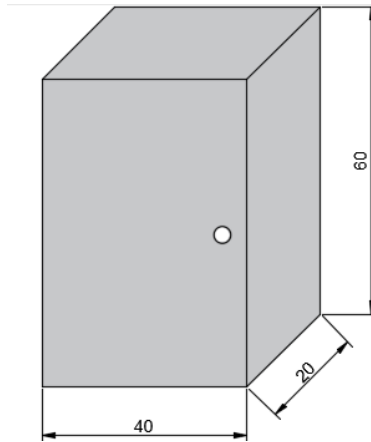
Dimensiones del Gabinete (Fuente Propia)
